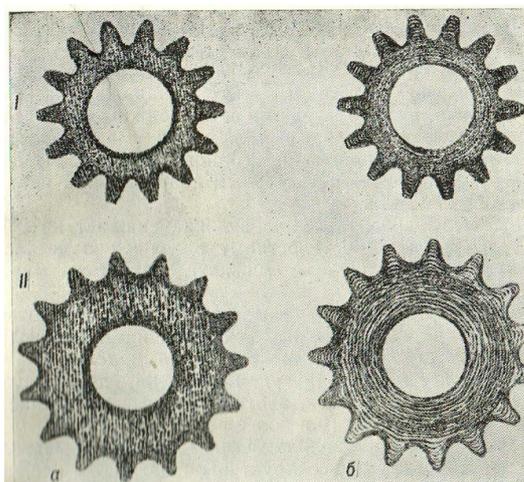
Макроструктура зубчатого колеса (I) и звездочки цепной передачи (II), изготовленных:
